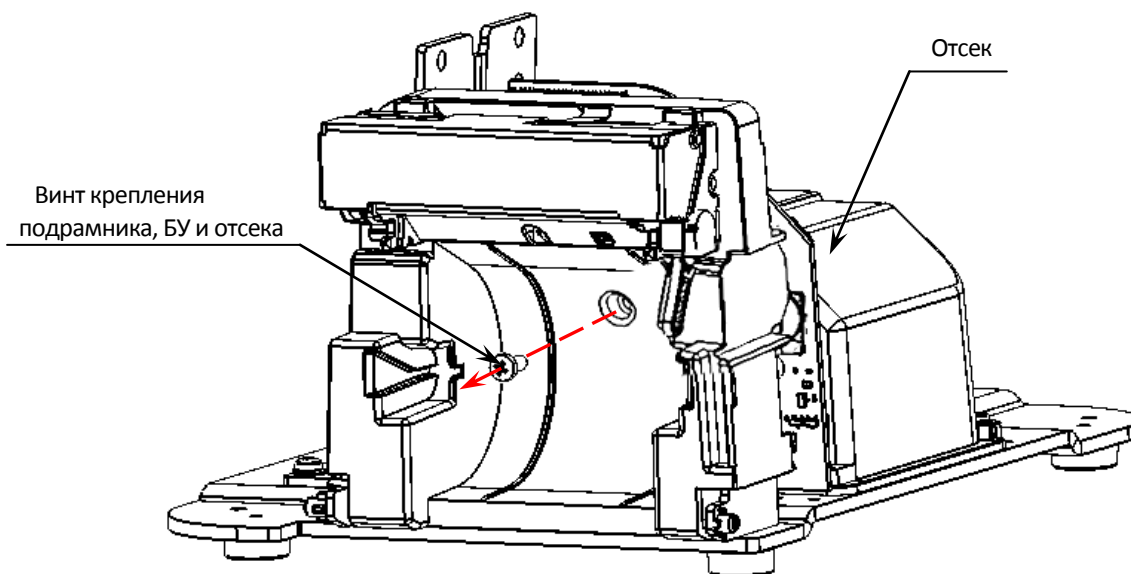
Винт крепления подрамника, блока управления и отсека в корпусе ККТ (крышка лотка для ЧЛ не показана)
